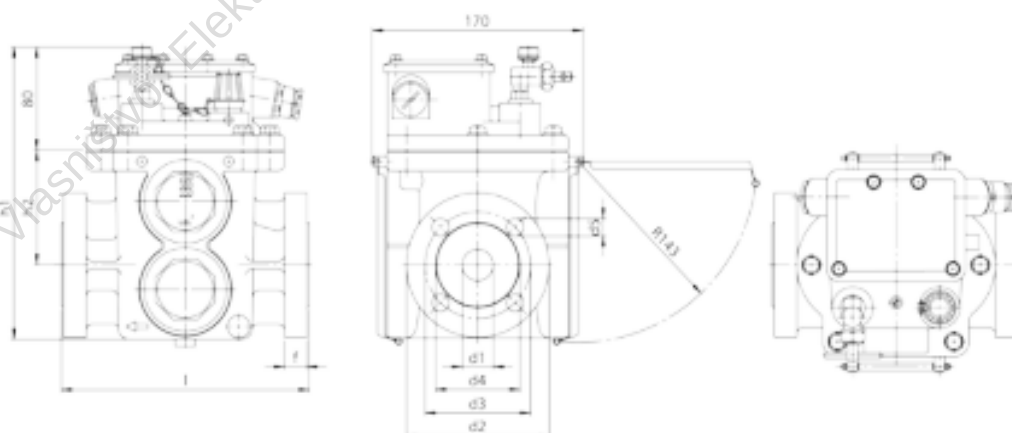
Dimensional drawing, type 05, 06, 07, 08, 09, 24
